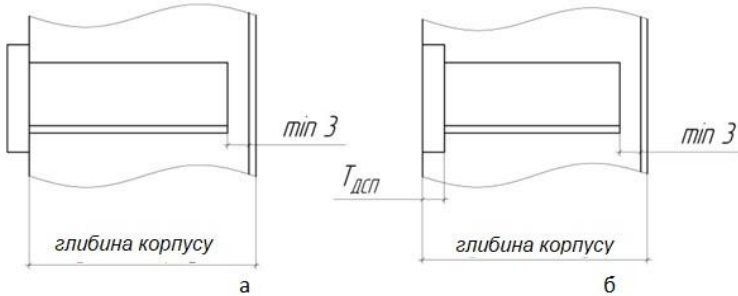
(а - для накладеного фасаду; б - для вкладеного фасаду)
